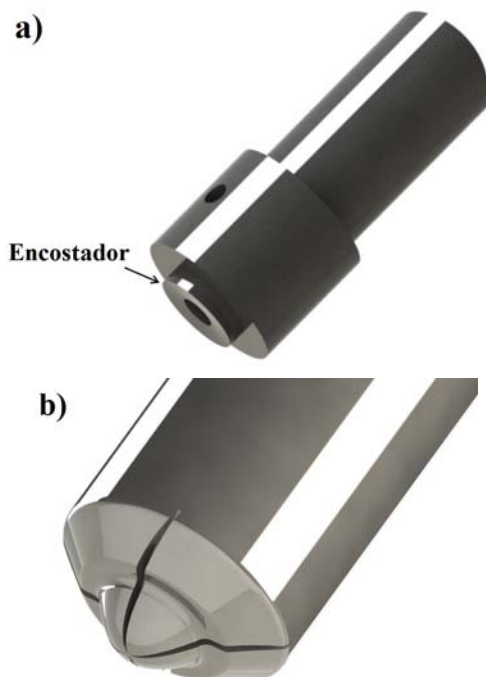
Geometria das ferramentas:a) encostador e o corpo da ferramenta; b) pino.
